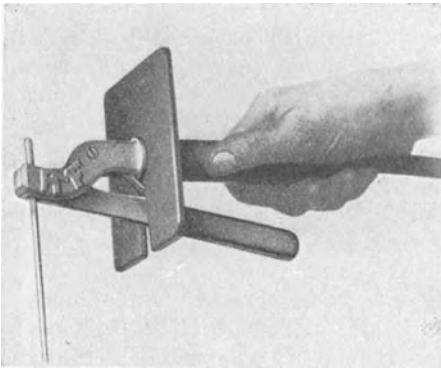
Schweißkolben für Kaltschweißungen.
